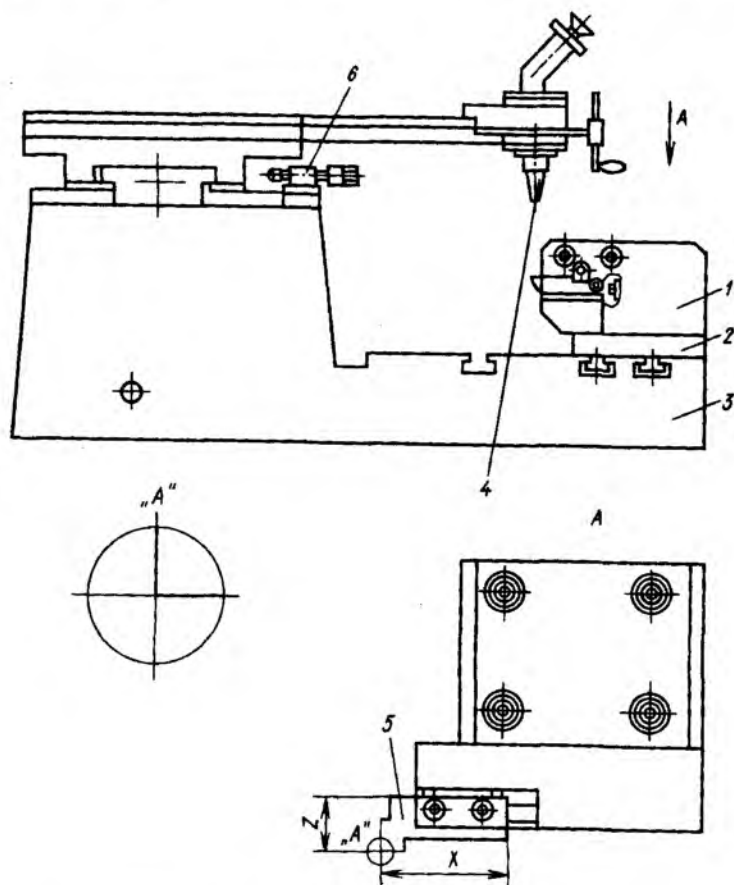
Устройство мод. БВ-2011 для настройки инструмента на размер
